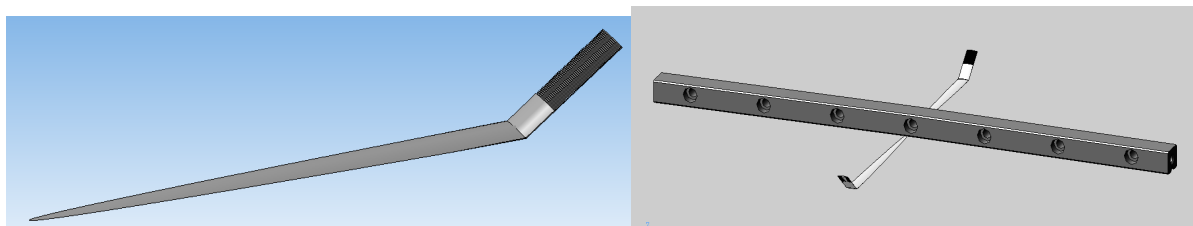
Компенсатор (а) и установка компенсаторов (б)
